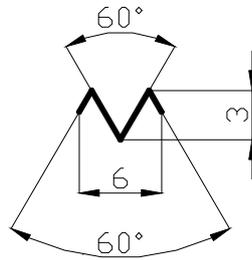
Условное обозначение рельефа рабочих поверхностей.
